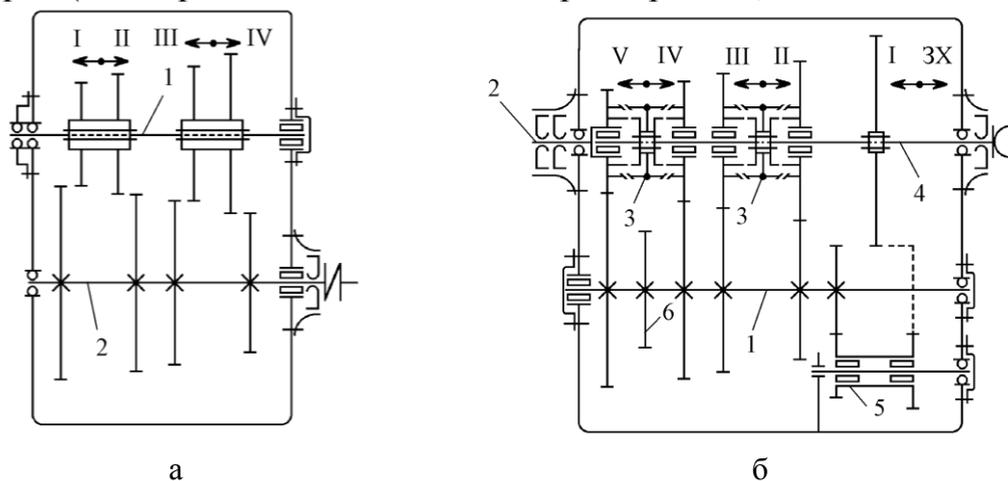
Схемы коробок передач: а – тракторной двухвальной: 1 – вал ведущий; 2 – вал ведомый; б – автомобильной: 1 – вал промежуточный; 2 – вал ведущий (первичный); 3 – синхронизаторы; 4 – вал ведомый (вторичный); 5 – блок шестерен реверса; 6 – шестерня привода лебедки; I...V – номер передачи
